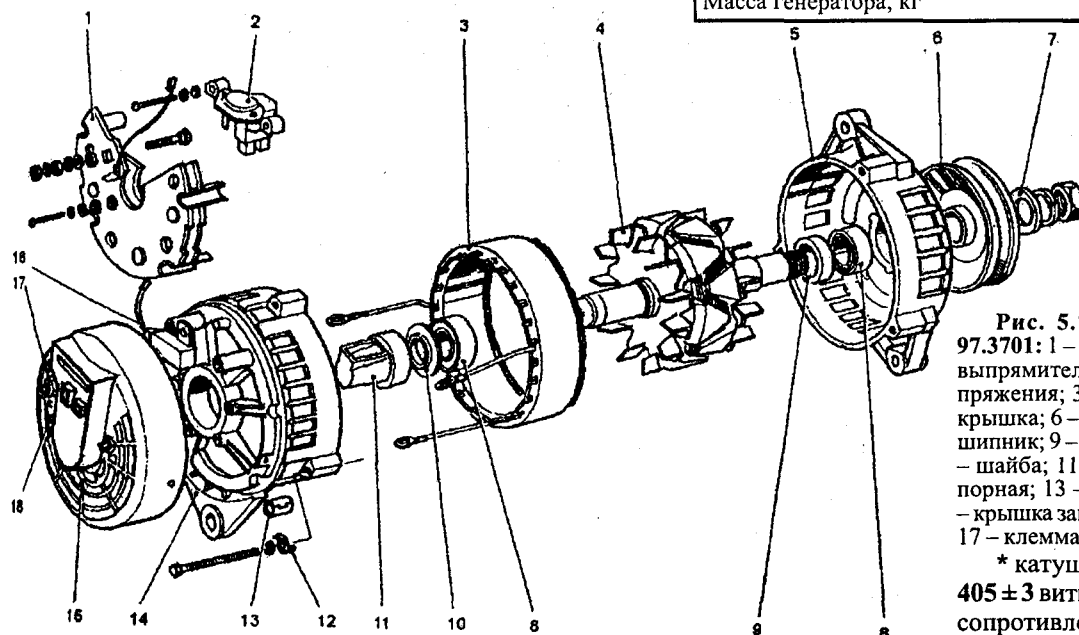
Детали генератора 97.3701: 1 - блок полупроводниковый выпрямительный; 2 - регулятор напряжения; 3 - статор, 4 - ротор; 5 - крышка; 6 - шкив; 7 - шайба; 8 - подшипник; 9 - втулка дистанционная; 10 - шайба; 11 - втулка; 12 - шайба стопорная; 13 - втулка; 14 - крышка, 15 - крышка защитная, 16 - конденсатор, 17 - клемма «+»; 18 - клемма «Д»
